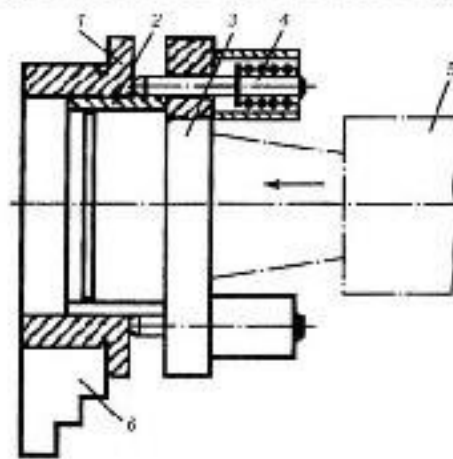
Схема установки свертной втулки: 1 — деталь; 2 — свертная втулка; 3 — оправка; 4 — штифты; 5 — пиноль задней бабки; 6 — патрон токарного станка
